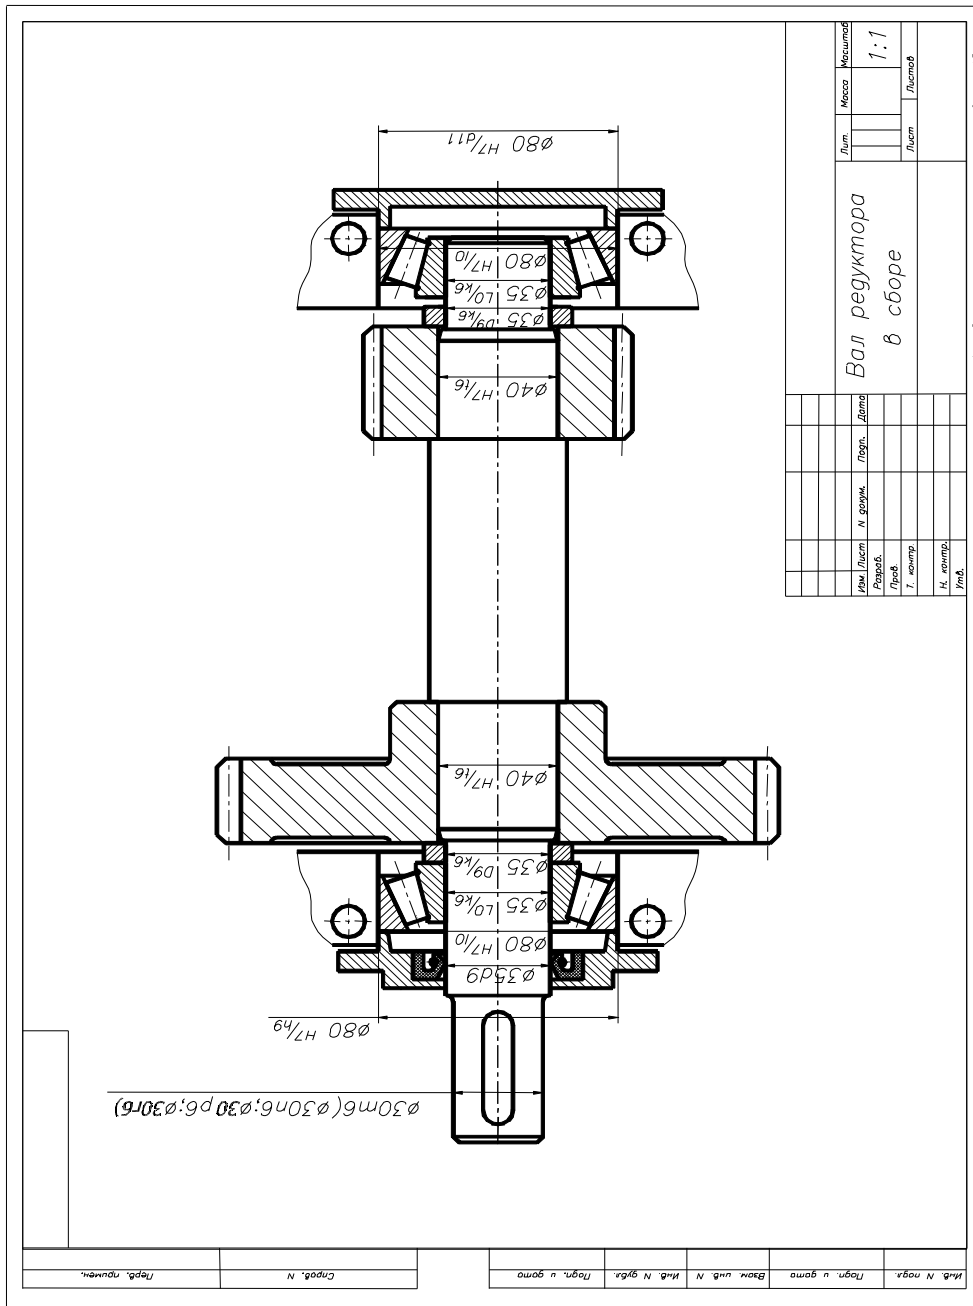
Рабочий чертеж узла вала редуктора
